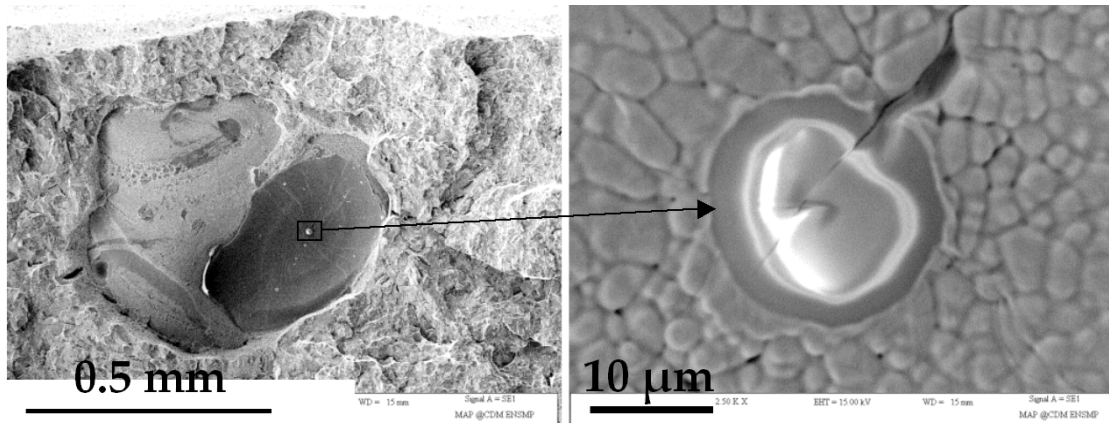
Défaut de soudage, soufflure à la ligne de fusion (RL FL_16)
